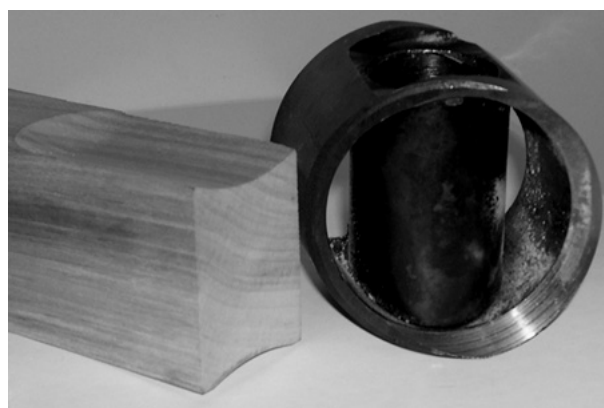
Конструкция дереворежущей фрезы с открытыми межзубовыми впадинами
